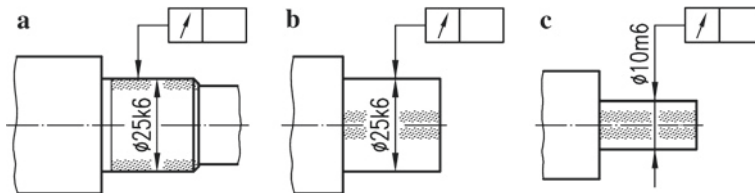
Bedeutung der Stellung des Toleranzpfeils. a sichtbares Geometrieelement toleriert (Rundlauf) b; c unsichtbares Geometrieelement (Achse) toleriert (Koaxialität)
